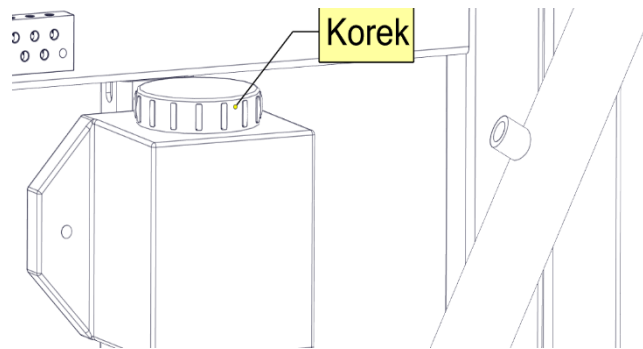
Масляный бак в системе автоматической смазки цепей
